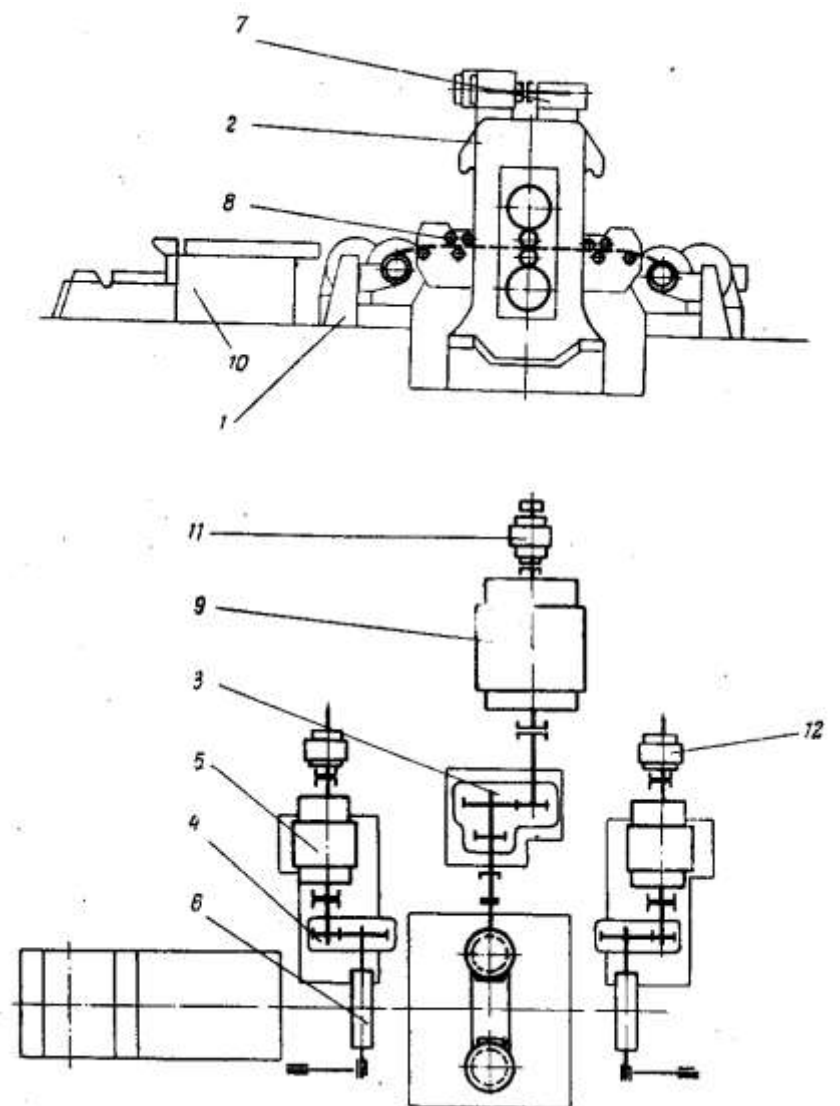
Кинематическая схема четырехвалкового реверсивного фольгопрокатного стана 160/450x750
